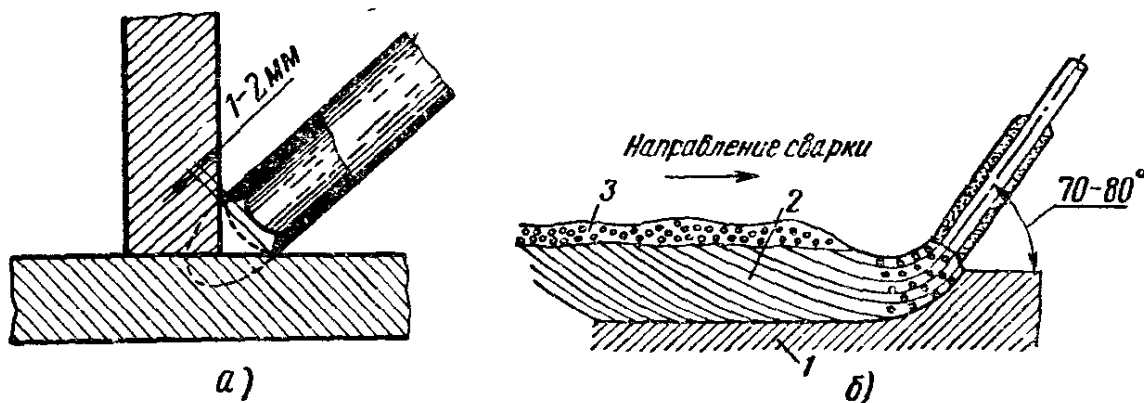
Положение электрода при сварке с глубоким проплавлением: а — поперечный разрез, б — продольный разрез: 1 — основной металл, 2 — металл шва, 3 — шлак
